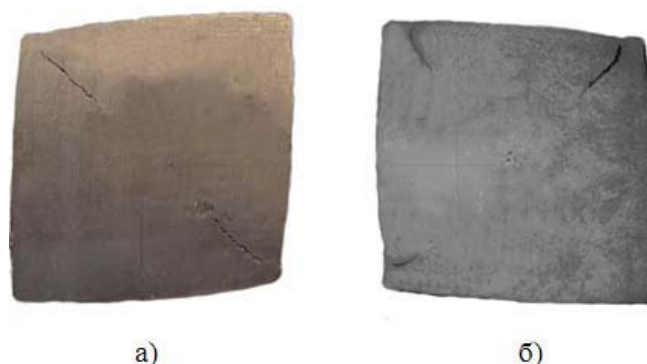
Внешний вид темплетов непрерывнолитых заготовок при развитии явления ромбичности
